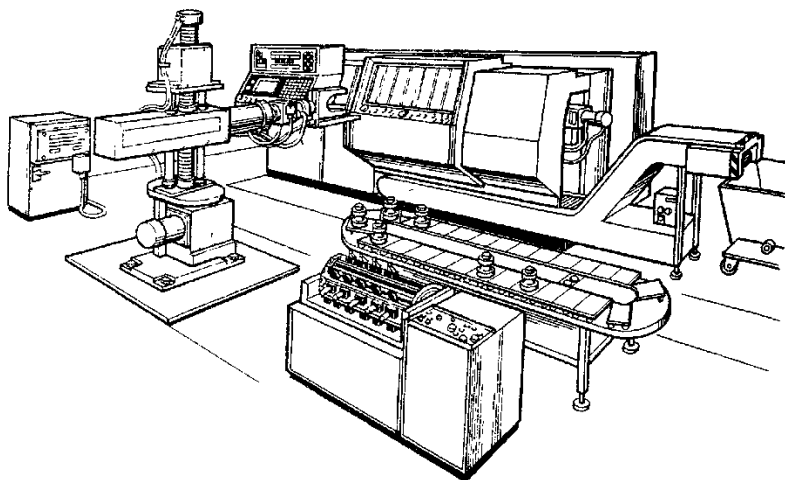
Гнучкий виробничий модуль з пристроями для заміни інструментів
